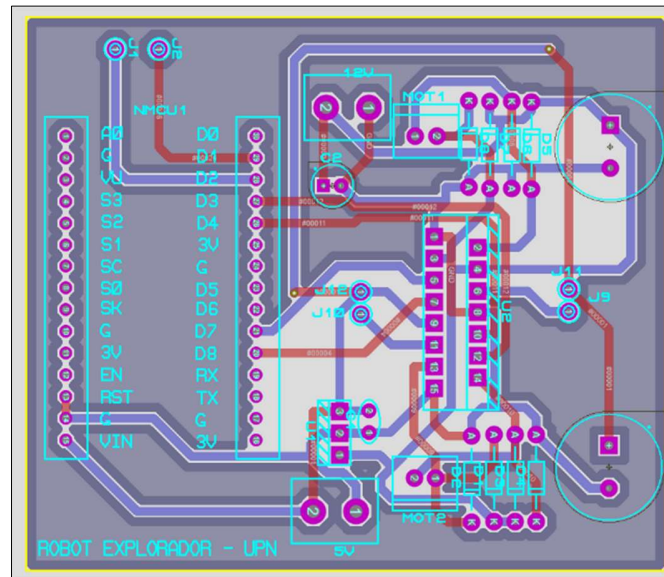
Diseño y ubicación de componentes electrónicos en PCB.
